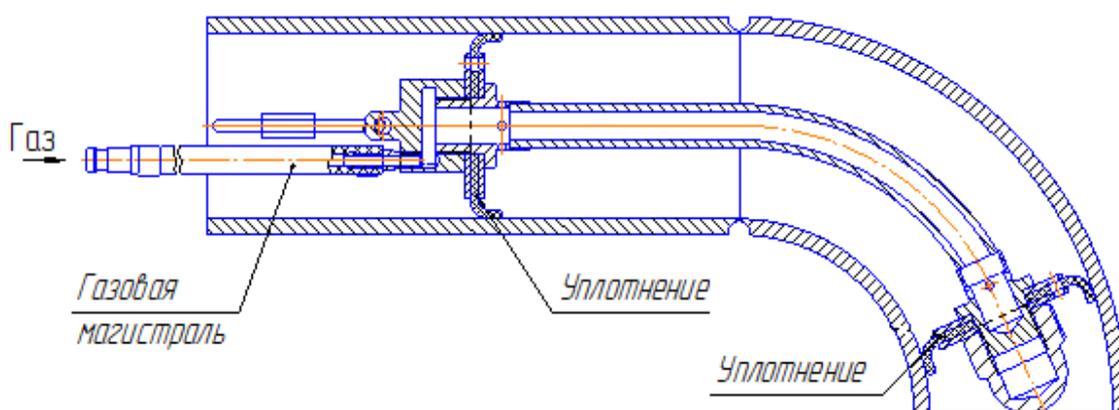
Схема установки устройства при сварке труб с отводами
